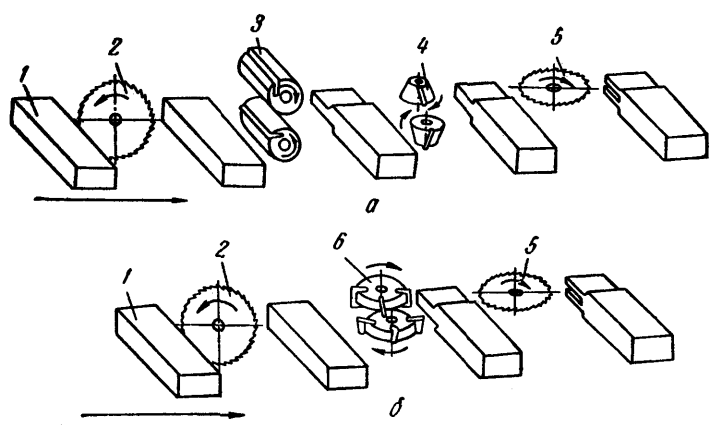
Принципиальная схема обработки детали на шипорезном станке ШО-6 с шипорезными и подсечными головками (а) и торцово-фрезерными головками (б).
